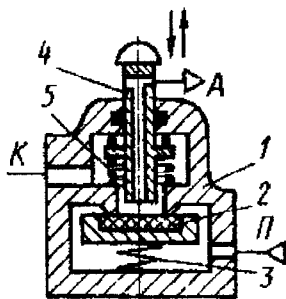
Схема трехканального клапанного распределителя: 1 - корпус, 2 - клапан мягкий, 3 - пружина, 4 - шток, 5 - пружина
